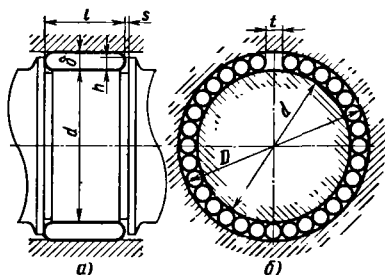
Конструктивные соотношения в игольчатых подшипниках
